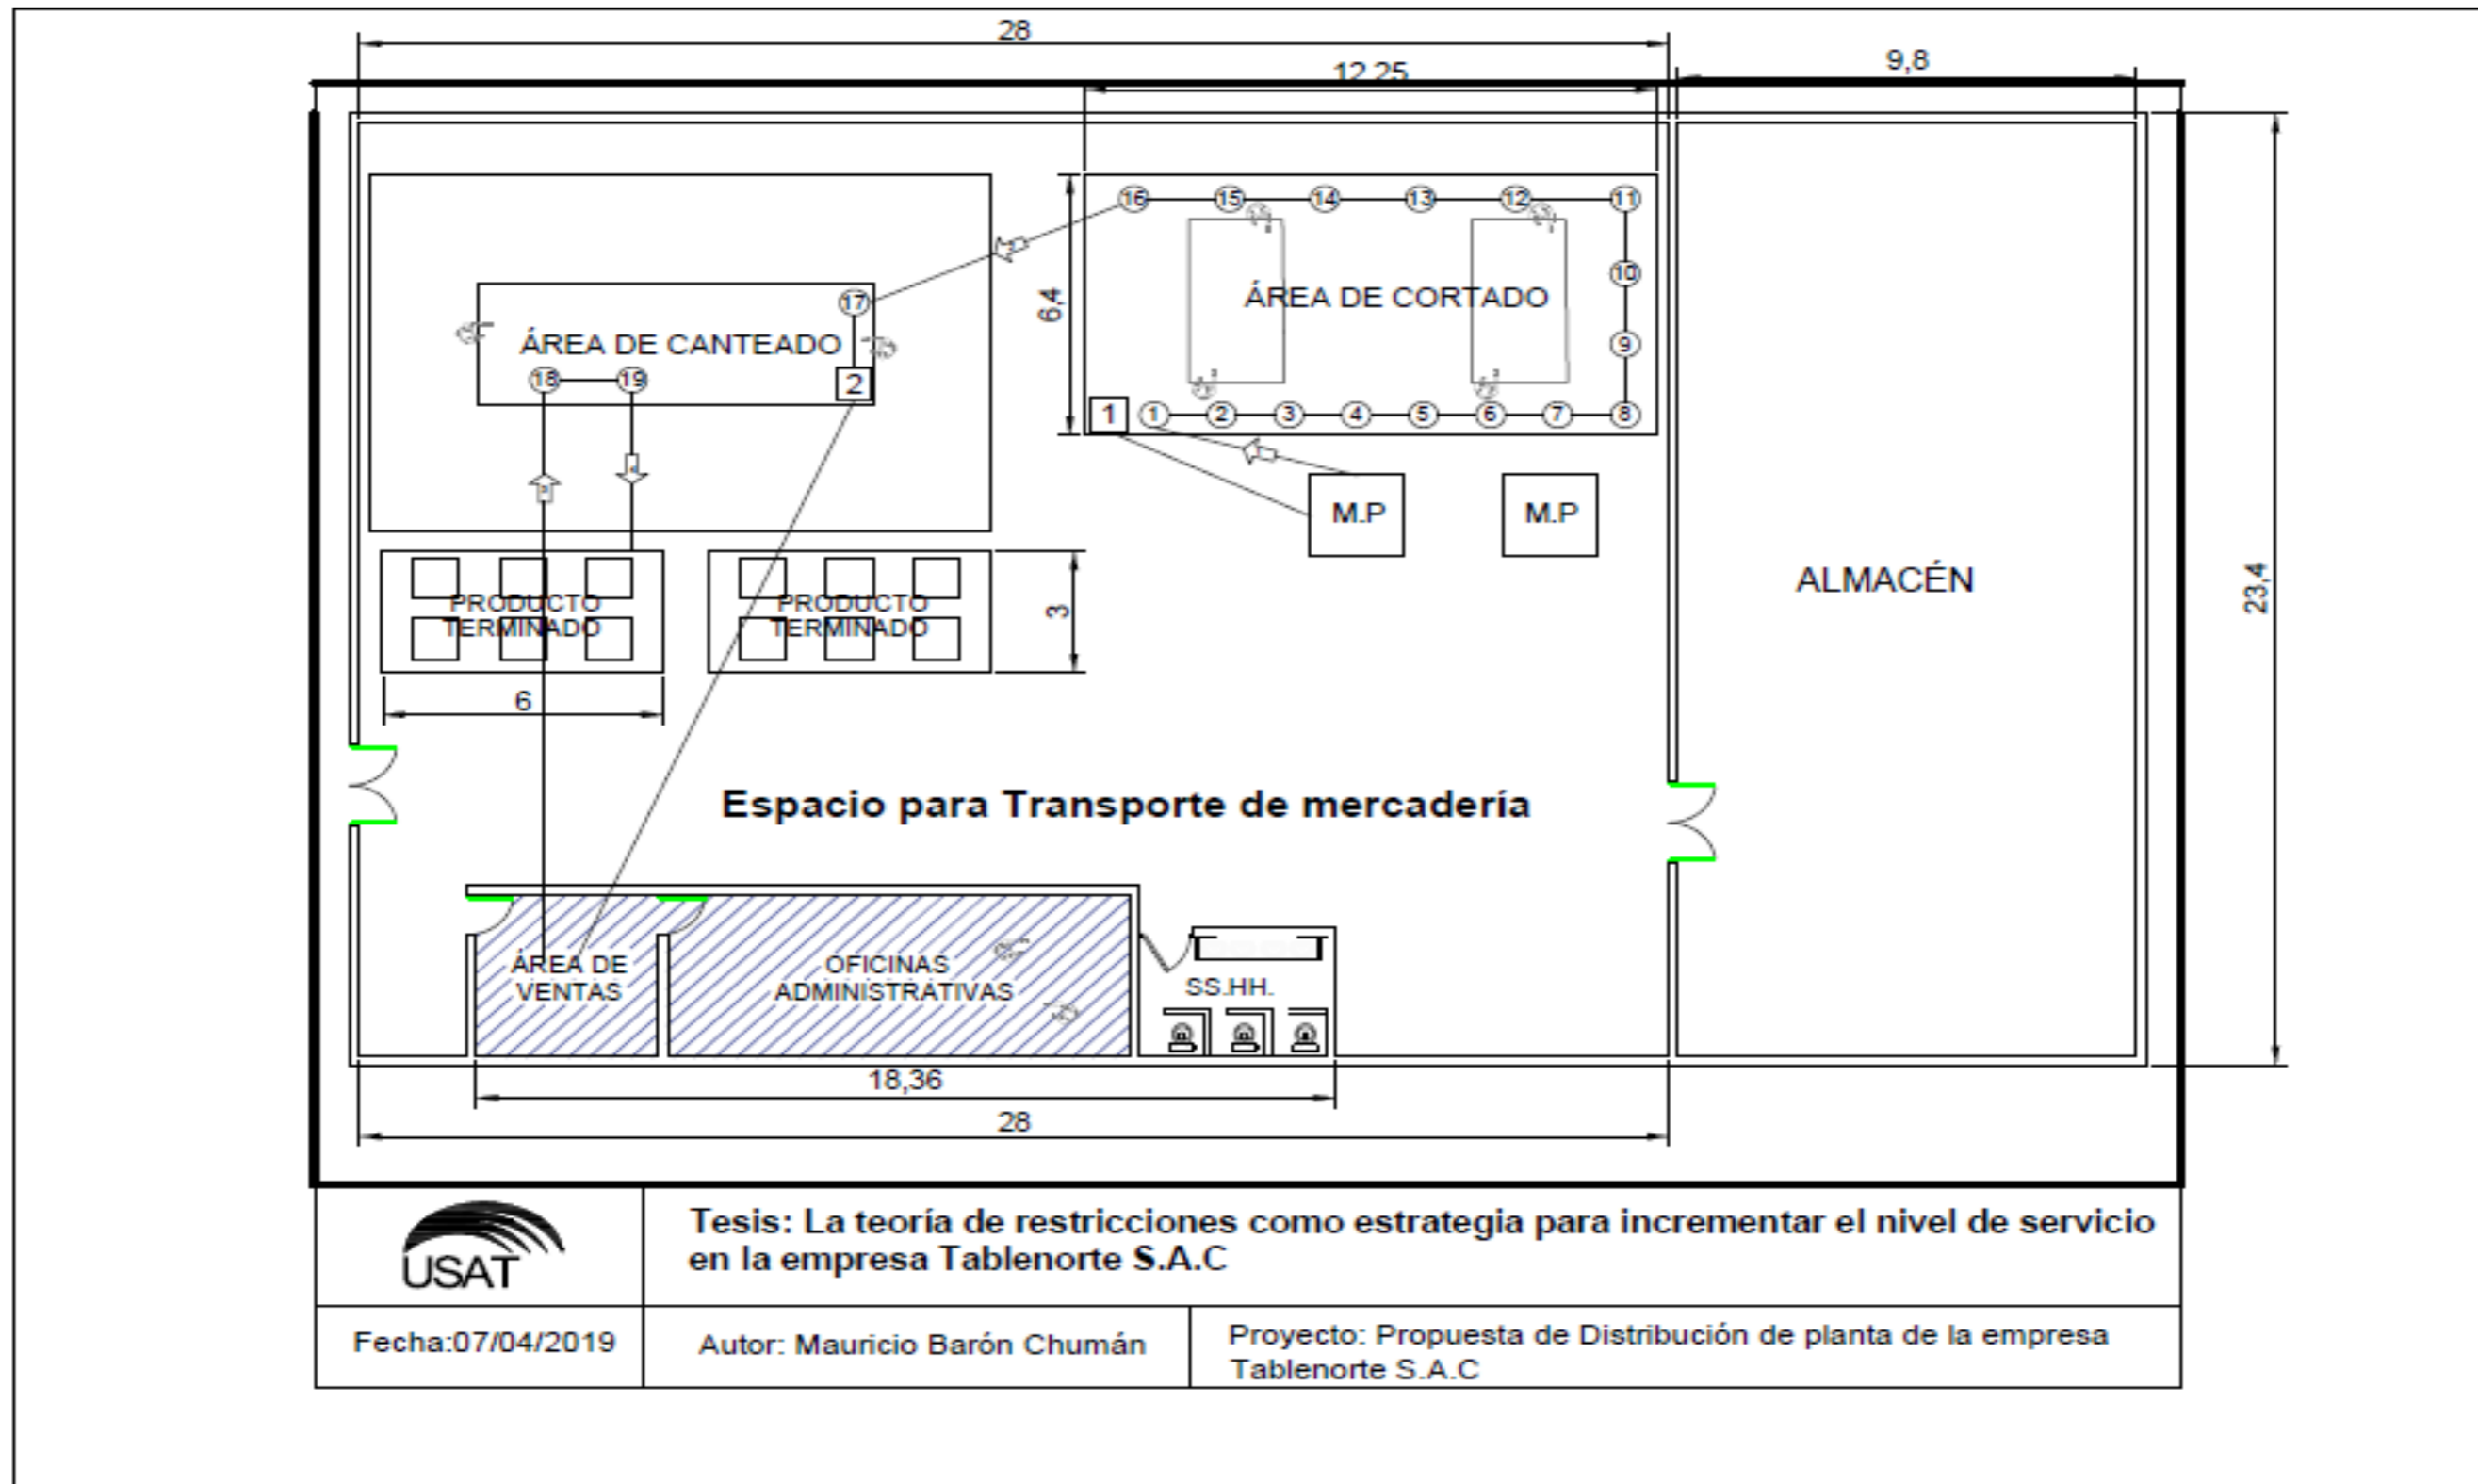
Propuesta de Distribución de planta en la empresa Tablenorte S.A.C.
